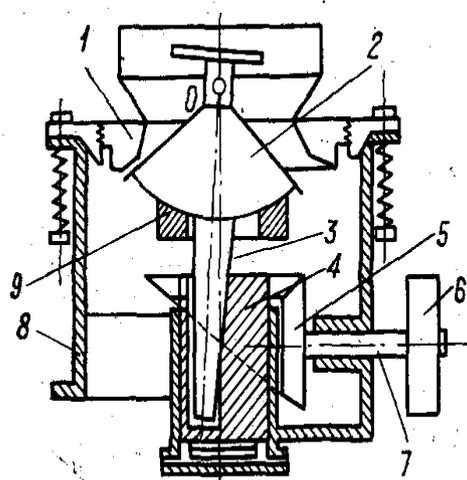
Схема конусной дробилки для среднего дробления с валом, подвешенным на сферическом подпятнике: 1 — коническая чаша; 2 — дробящий конус; 3 — вал; 4 — эксцентриковый стакан; 5 — коническая передача; 6 — шкив; 7 — приводной вал; 8 — станина; 9 — подпятник
